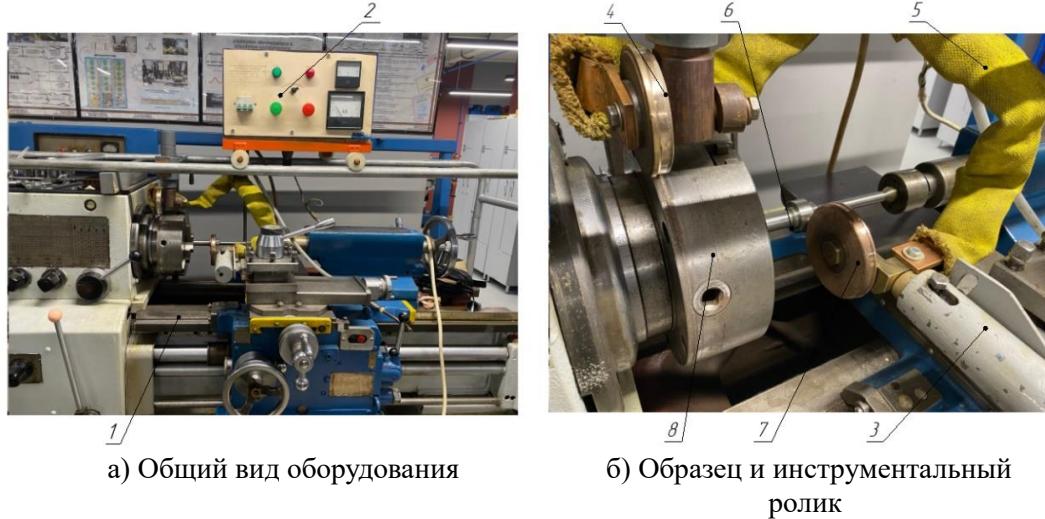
Фрагмент размещения оборудования и процесса ЭМПЗ образцов на токарно-винторезном станке 16К20;
